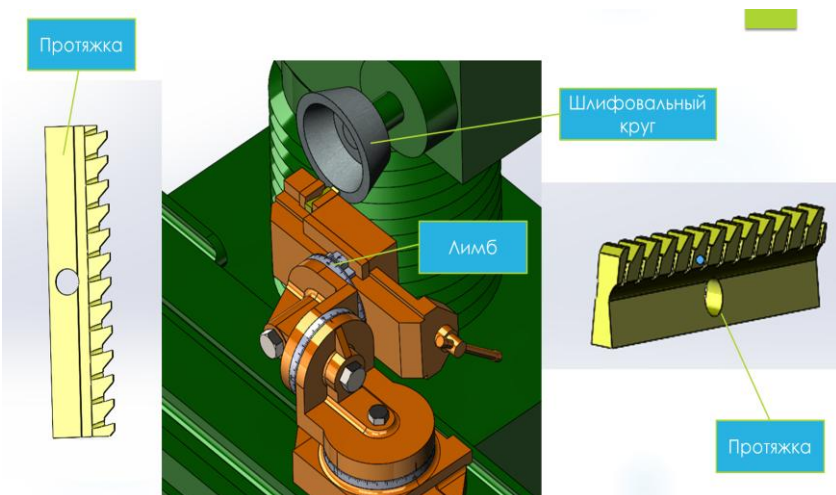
Наладка станка на заточку плоской протяжки по задней поверхности
